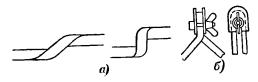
Правка головки. а — формы головки; 6 — приспособление для правки.
